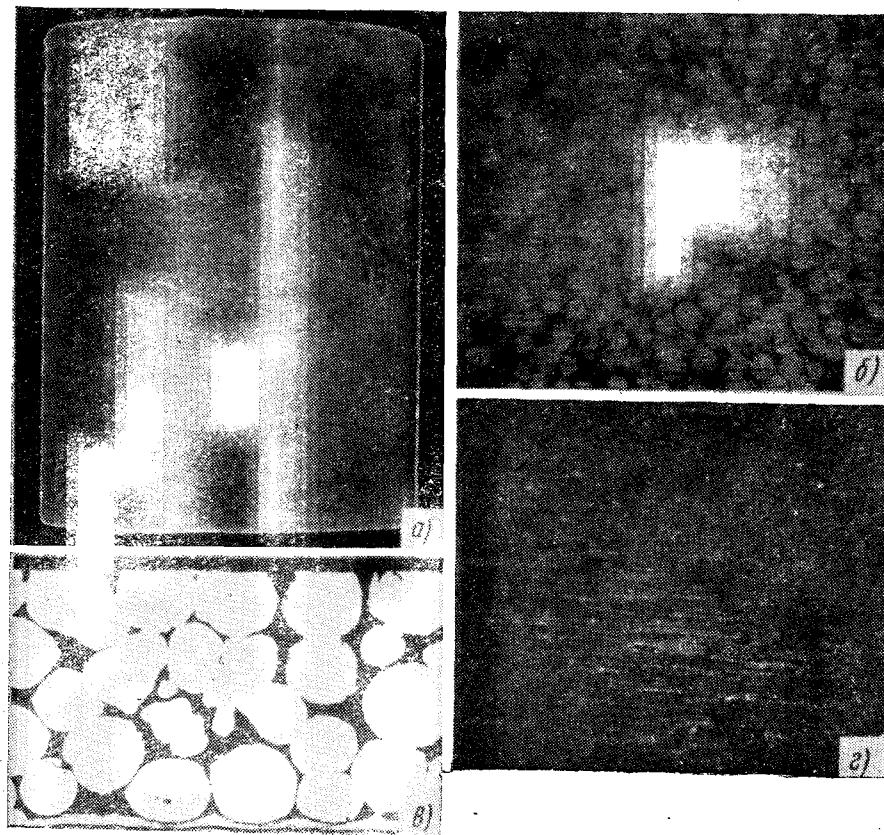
Неравномерность срабатывания рабочего слоя подшипника по его длине: а — общий вид ( $\times 0,8$ ); б — вид поверхности наиболее нагруженного участка ( $\times 40$ ); в — микрошлиф поперечного сечения наиболее нагруженного участка ( $\times 100$ ); г — вид поверхности центрального участка
